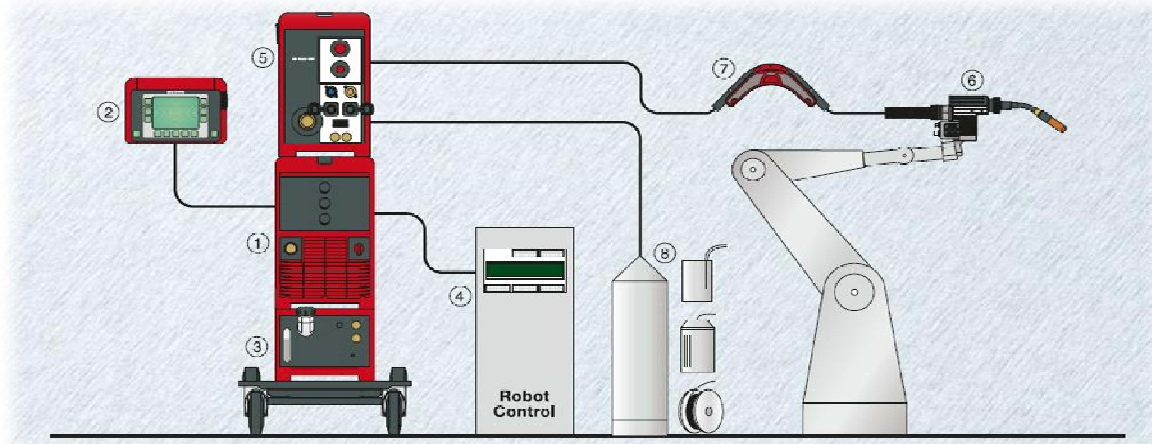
Equipamento CMT para um sistema de soldadura robotizado [10].
